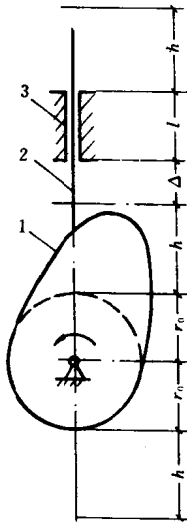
直动从动杆盘状凸轮的纵向尺寸
